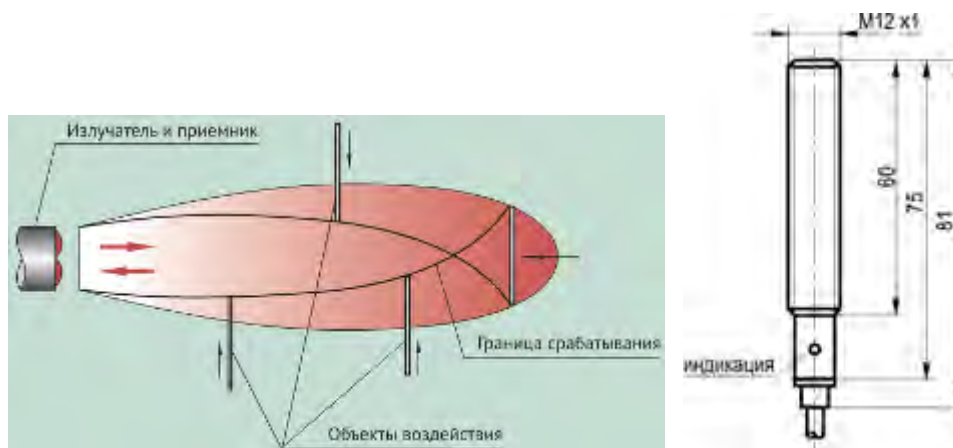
Общий вид и габаритный чертеж датчика OV A25A-31N-100-LZ
